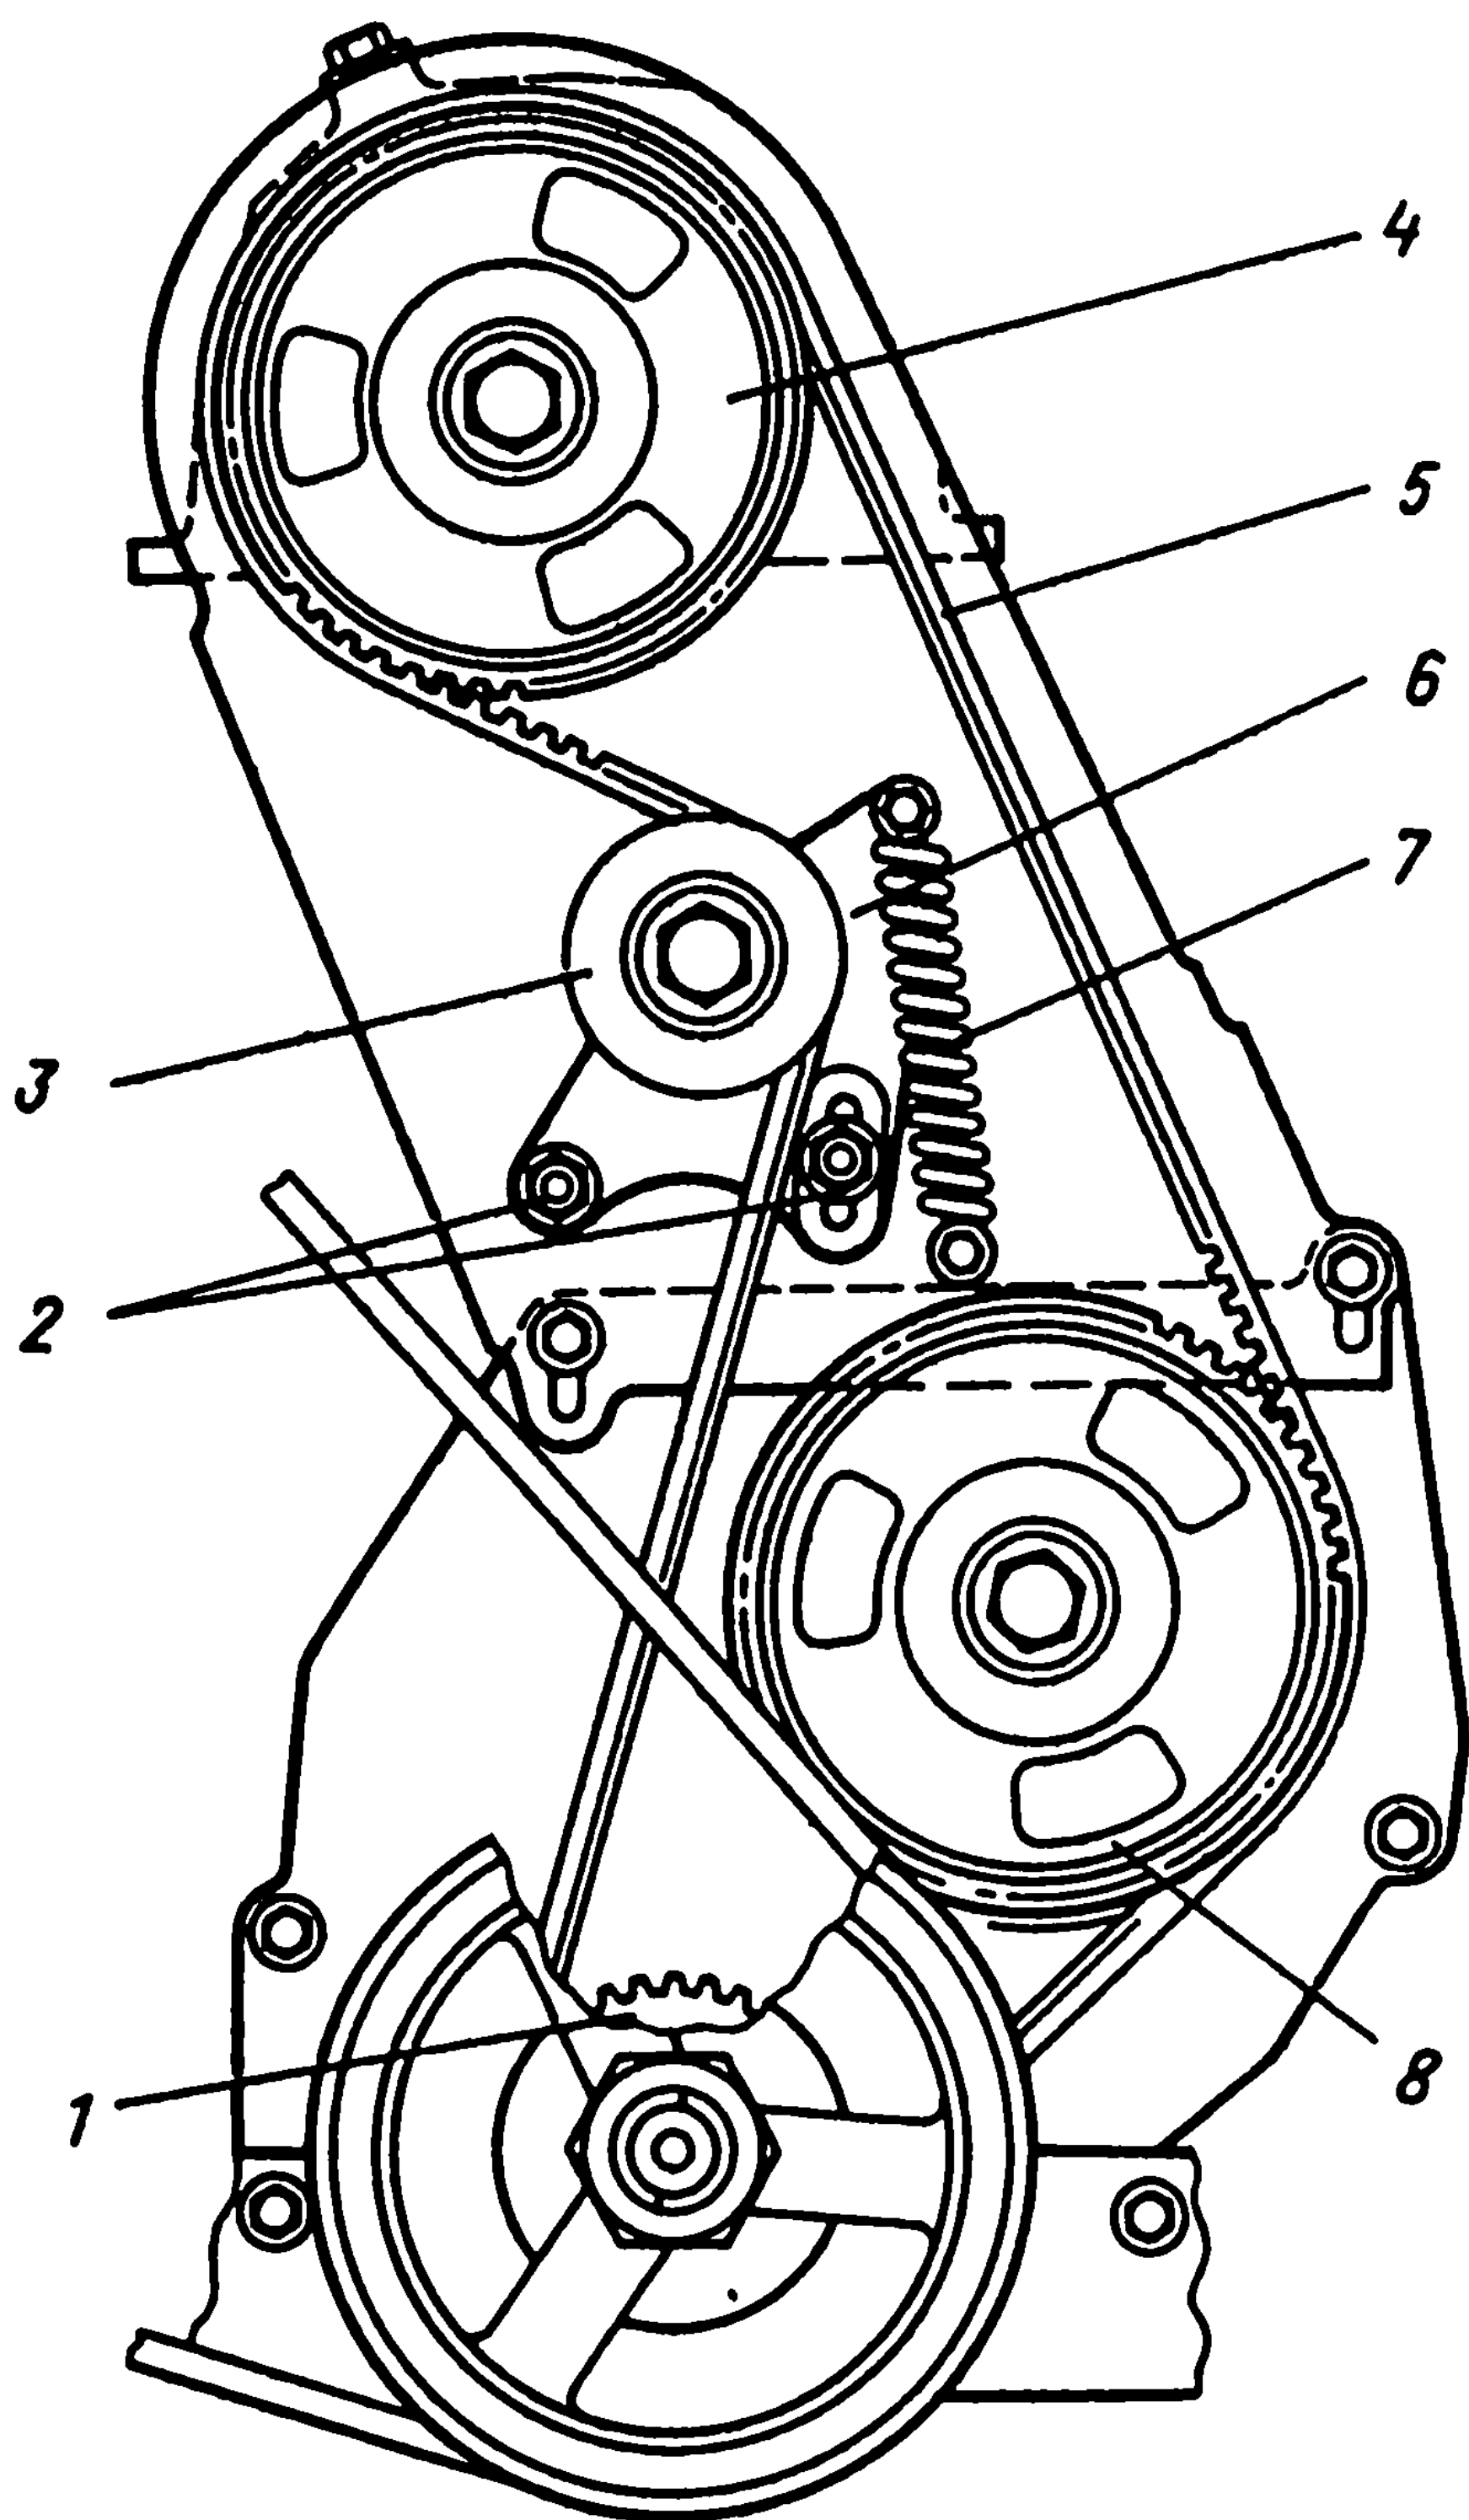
Привод распределительного вала двигателя ВА3-2105
